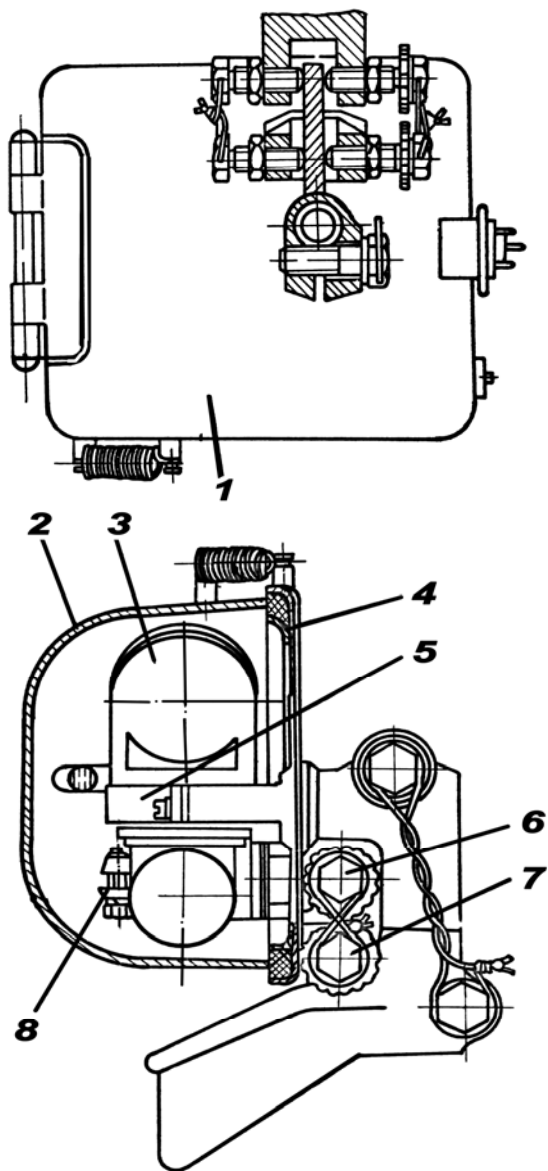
Установка коллиматорного прицела К10–Т:
